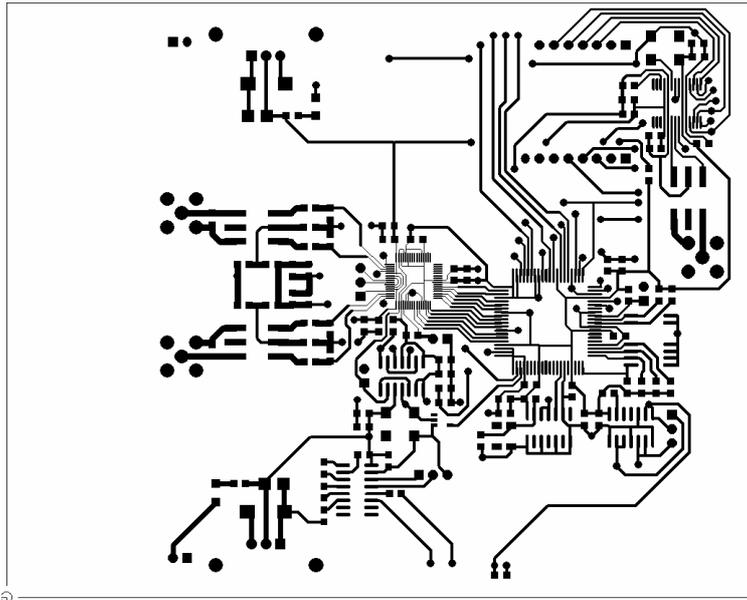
Vista superior do PCB da placa desenvolvida.
